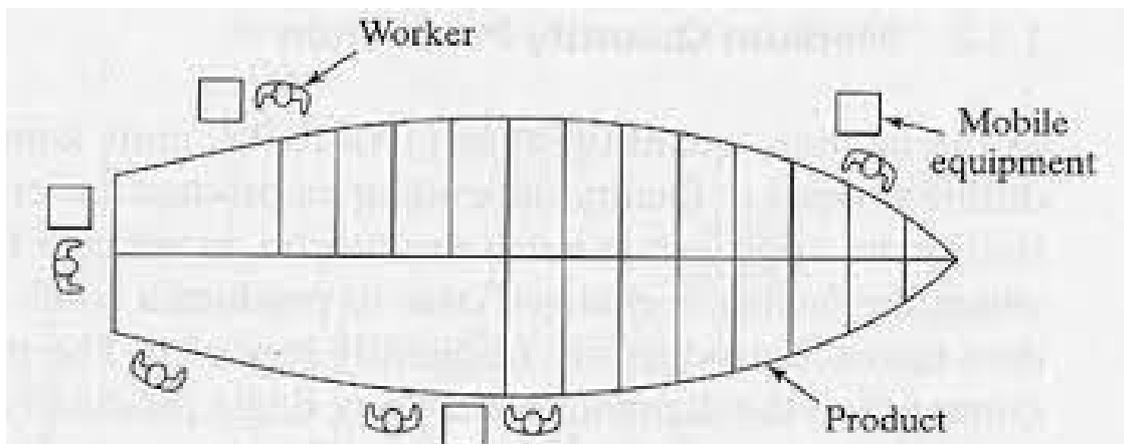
Esempio di layout a punto fisso [Immagine tratta da: Maraschi (2011)]
